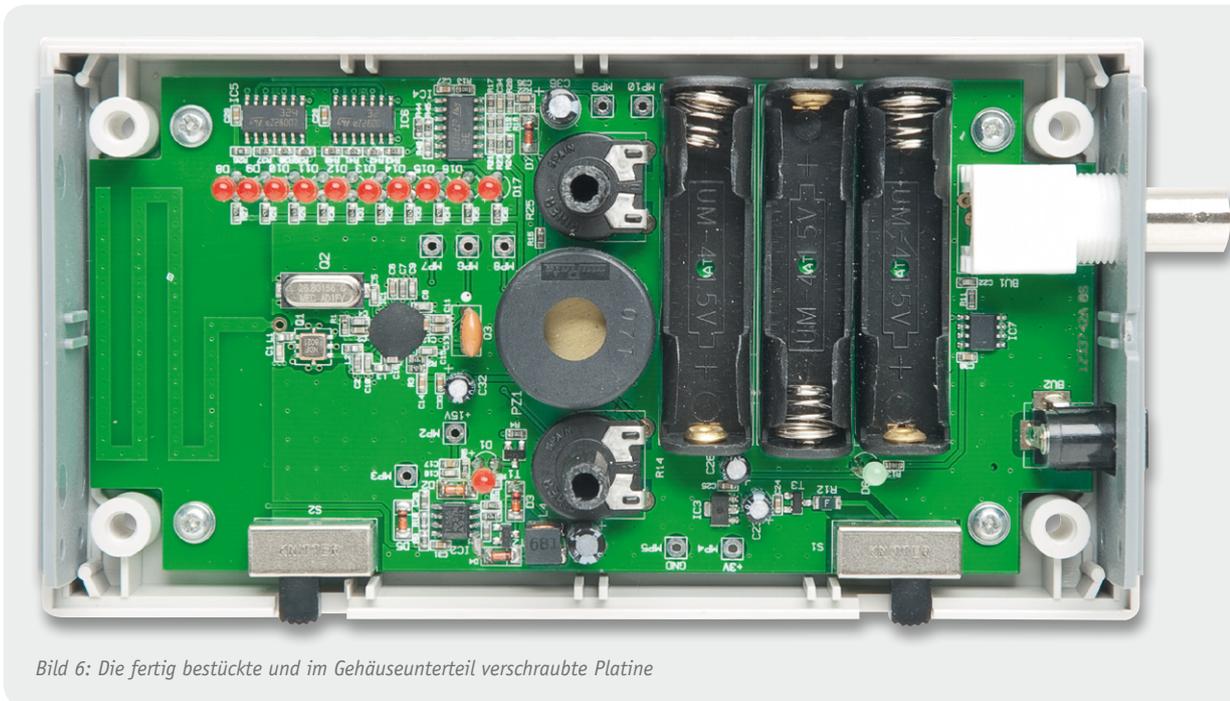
Die fertig bestückte und im Gehäuseunterteil verschraubte Platine
